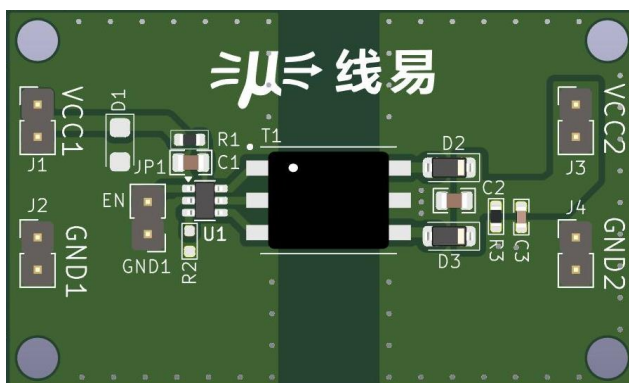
PCB 示意图(尺寸: 30x 50mm)
